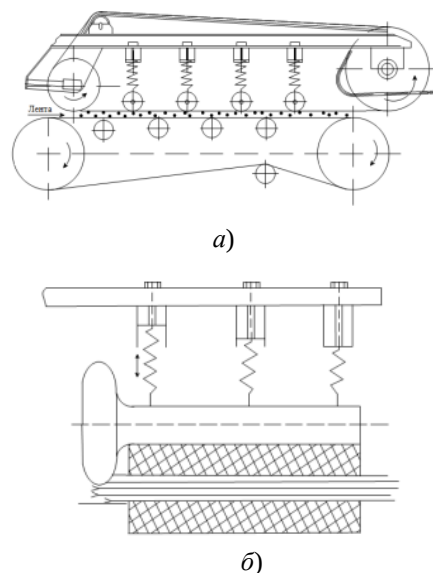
Схема усовершенствованного зажимного транспортера: а – общий вид; б – вид ролика с выступом
